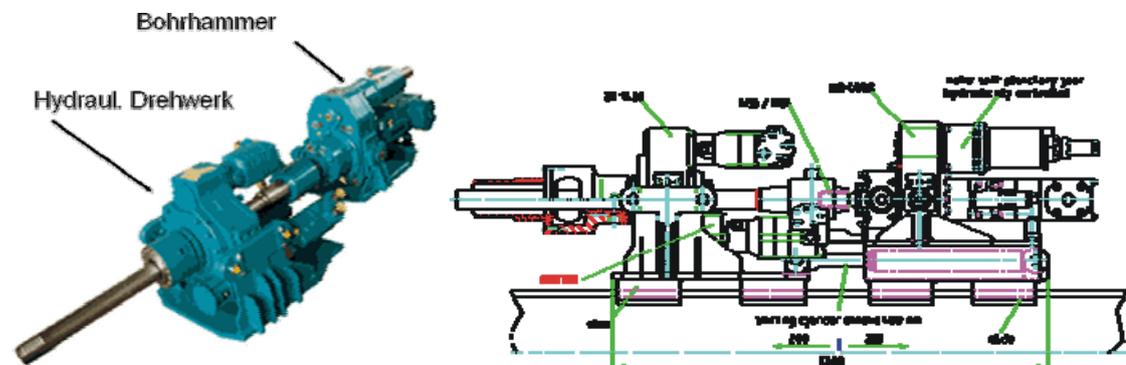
Drehwerk für verrohrtes Dreh-Schlagbohrverfahren [13]
